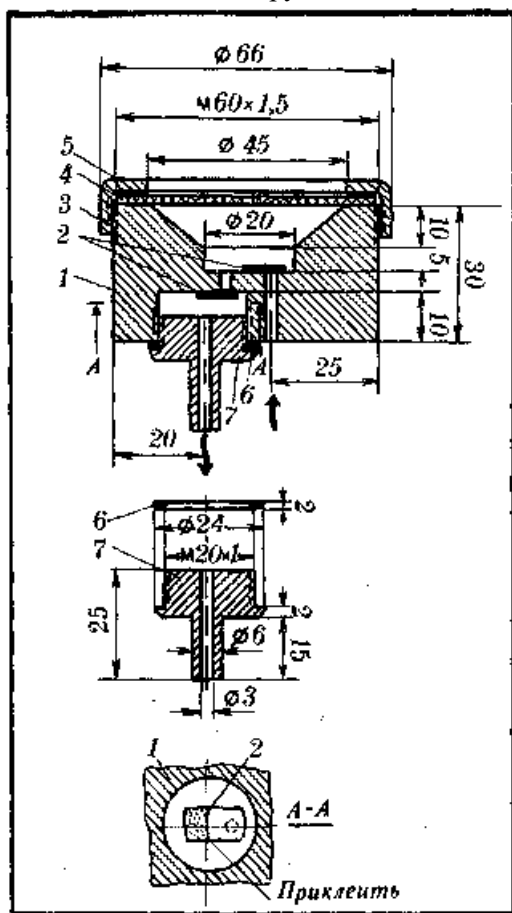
Устройство помпы: 1 — корпус; 2 — клапаны; 3 — крышка; 4 — диафрагма; S — кольцо-прокладка; 6 — прокладка; 7 — штуцер
